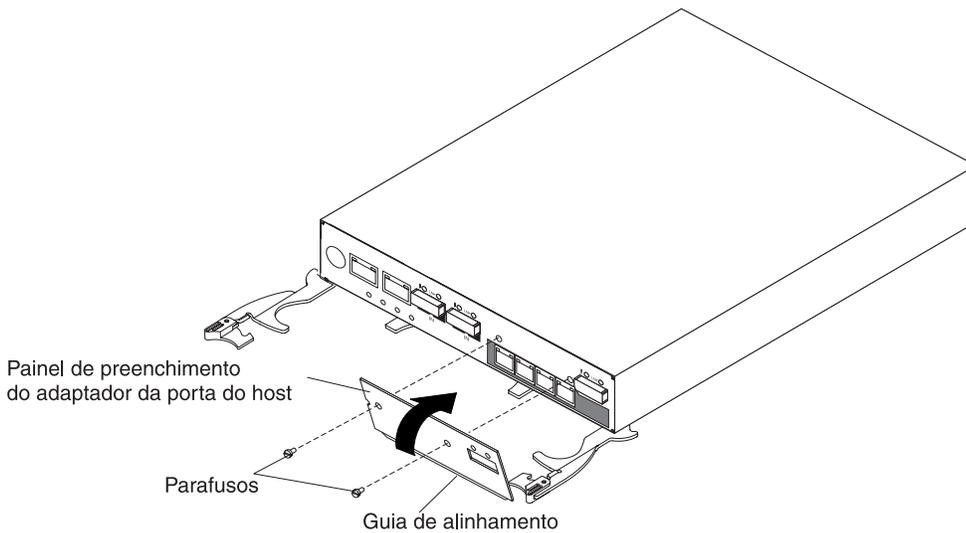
Removendo o Painel de Preenchimento do Adaptador de Porta do Host
